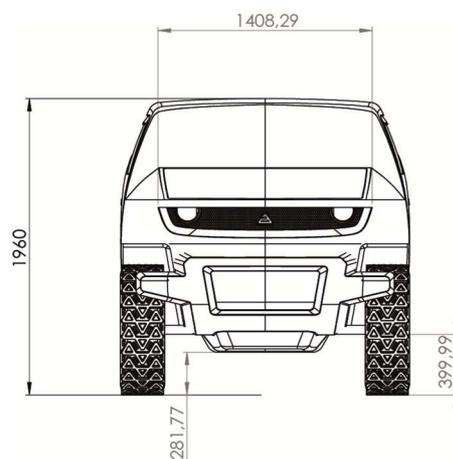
Vista frontal. Escala 1/50; dimensões em milímetros. Fonte: autor.
